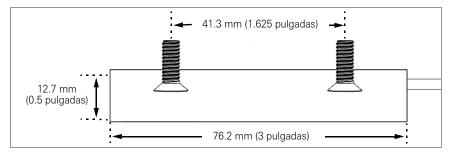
Dimensiones del ensamblaje de la cubierta
